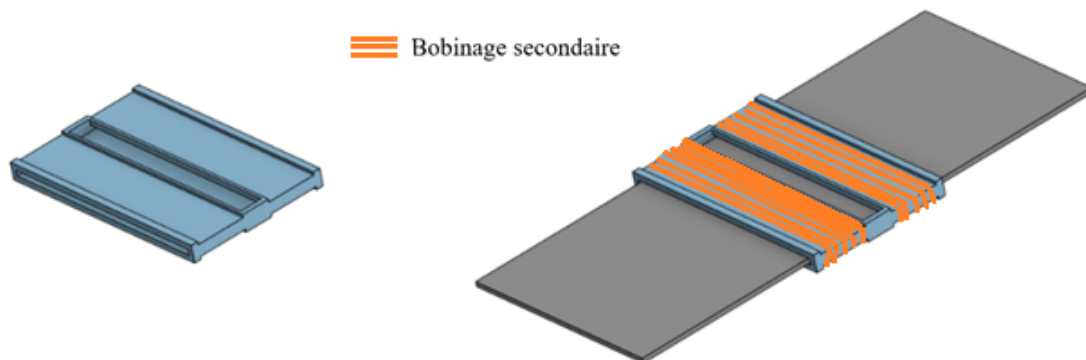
Présentation du support de bobinage seul (gauche) et du support bobiné avec l'échantillon inséré (droite)
